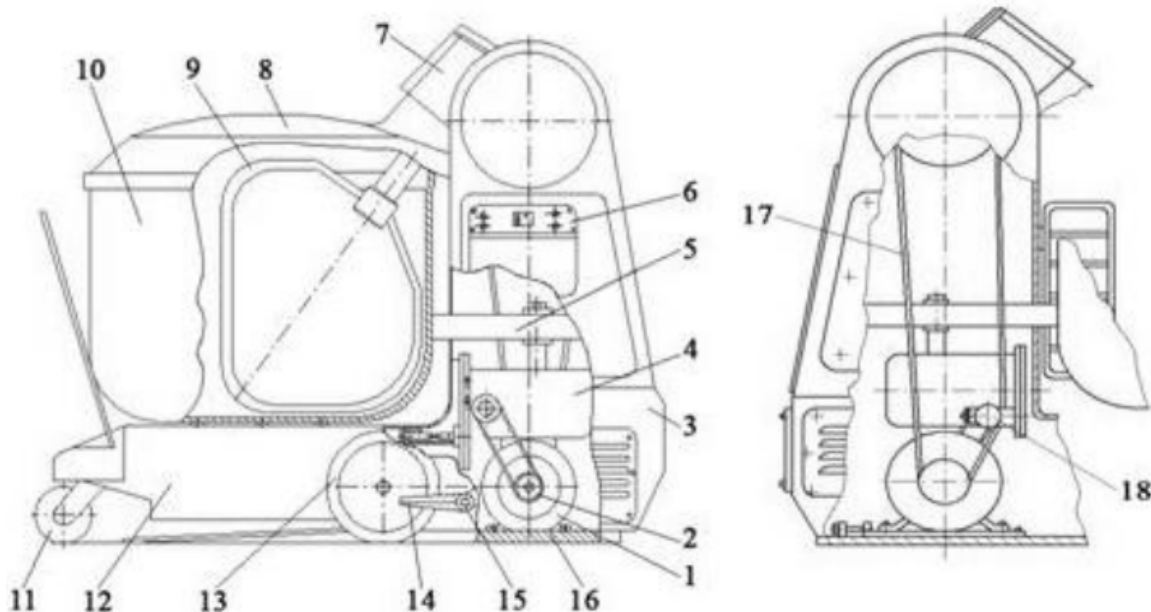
Машина тістомісильна МБТМ-140-01: 1 - електродвигун; 2, 17 - клінопасові передачі; 3 - корпус; 4, 7 - черв'ячний редуктор; 5 - ролик; 6 - пост управління; 8 - кришка; 9 - місильний орган; 10 - дежа; 11 - колесо поворотне; 12 - візок; 13 - колеса неповоротні; 14 - педаль; 15 - гаки; 16 - плита опорна; 18 - ролик натяжний
